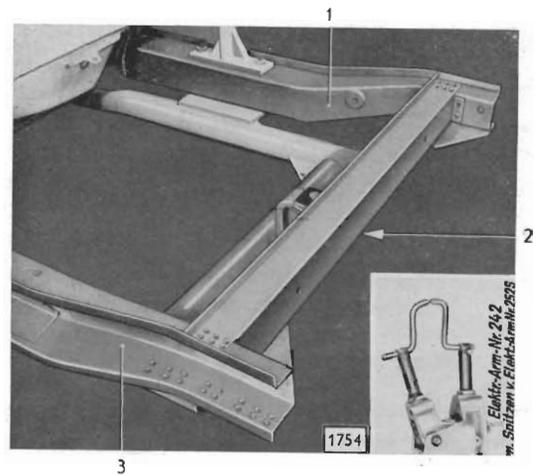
Vorderrahmenquerträger an Längsträgern zangenpunktgeschweißt
